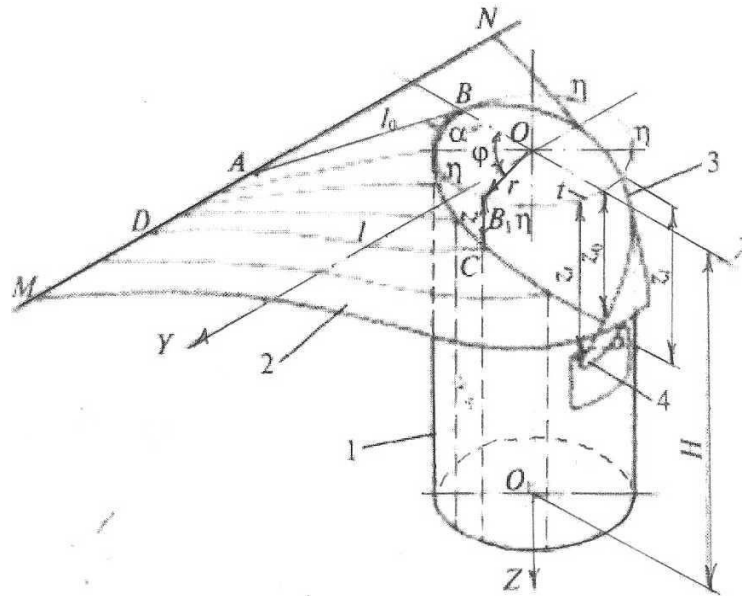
Розрахункова схема рукавоутворювача
